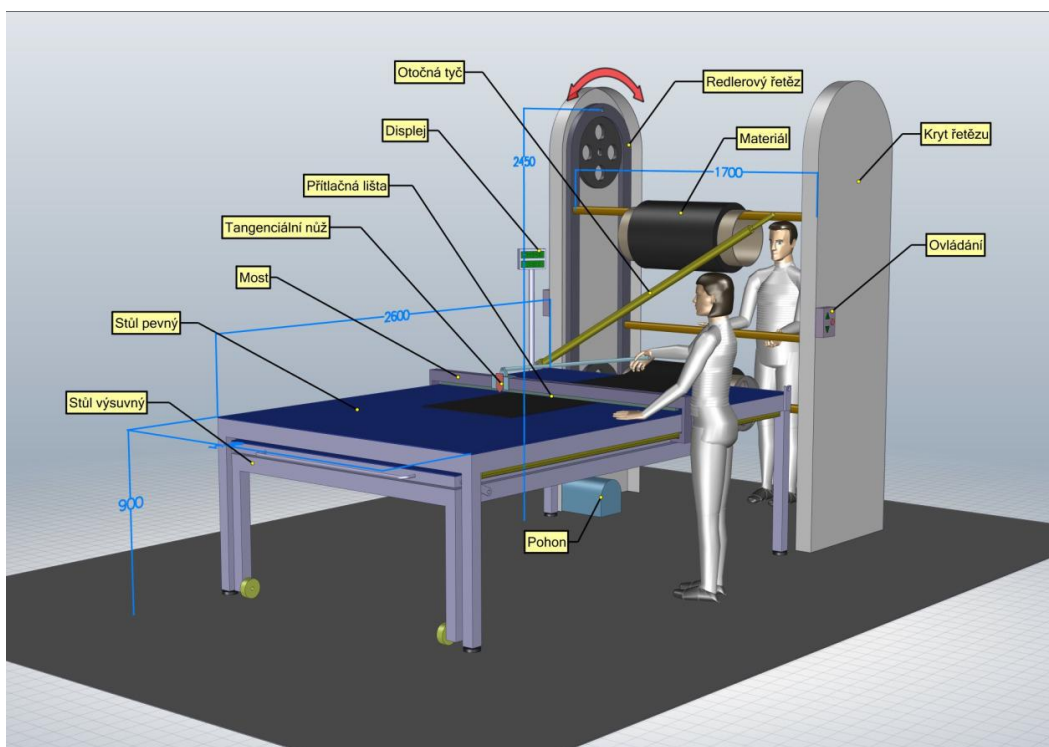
CNC Řízený stůl firmy Zünd [9]
